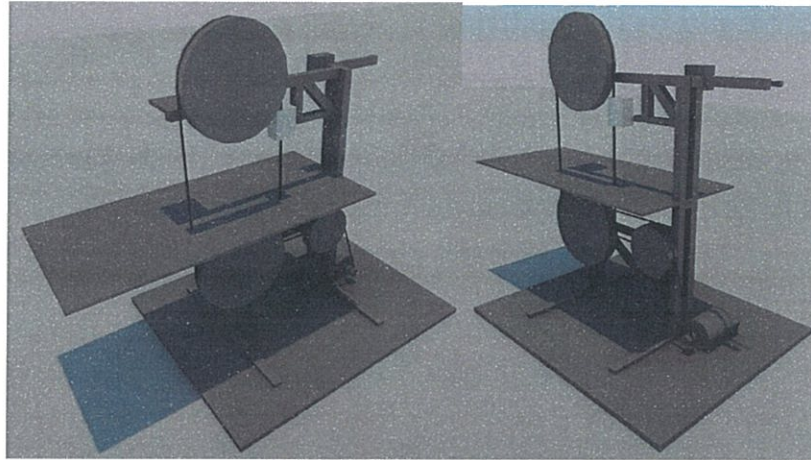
Diseño de la estructura del prototipo (máquina cortadora de carne)
